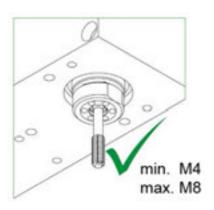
Einsatzbereich Gewindeformwerkzeug
